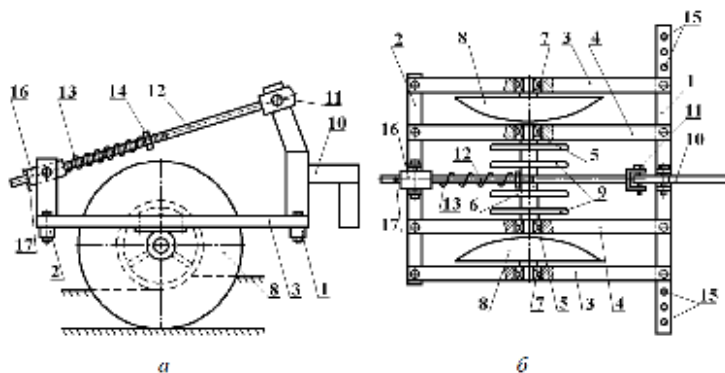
Каток: *а* – вид сбоку; *б* – вид сверху; 1, 2 – балки поперечные; 3, 4 – балки продольные; 5, 7 – подшипники; 6 – ось; 8 – сферические диски; 9 – прикатывающие кольца; 10 – кронштейн; 11 – палец; 12 – штанга; 13 – пружина; 14 – гайка; 15 – регулировочные отверстия; 16 – муфта; 17 – шплинт
